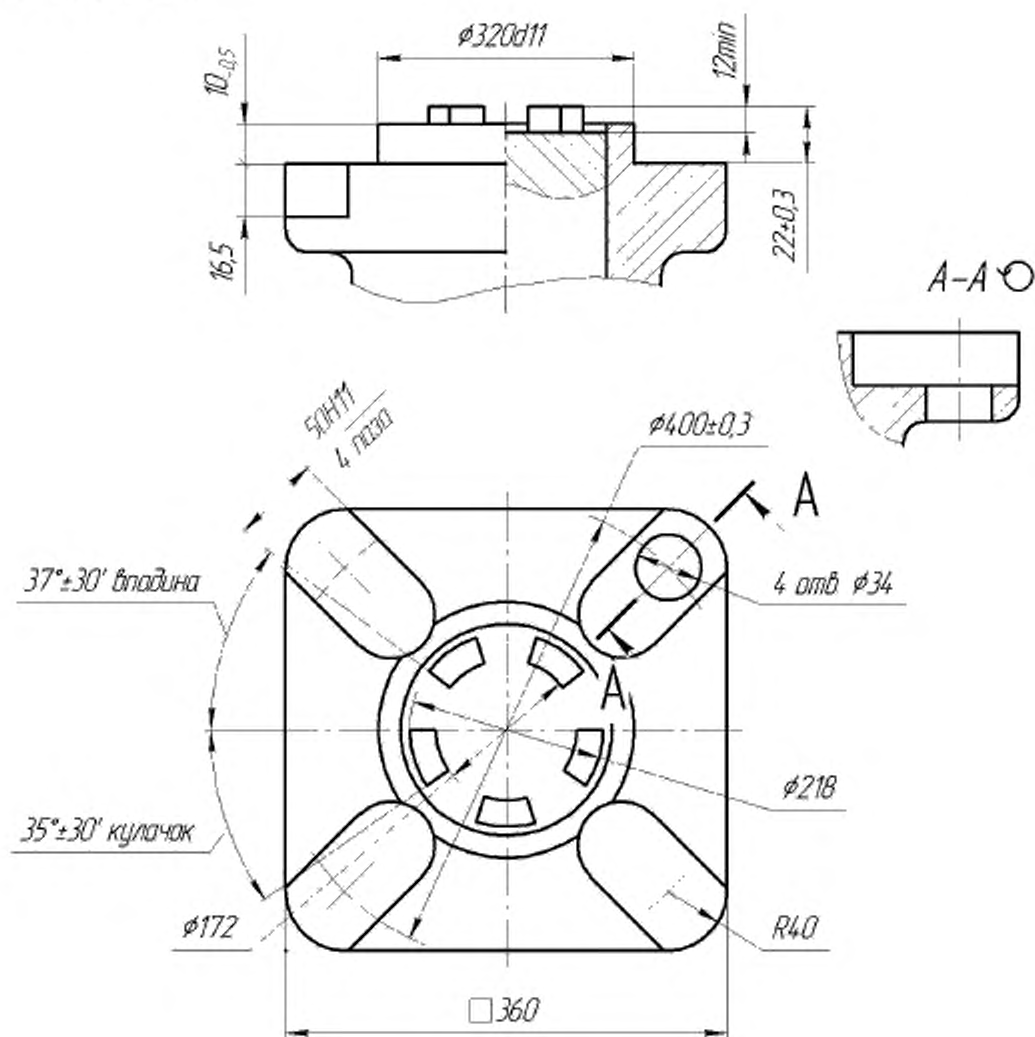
Ответное присоединение трубопроводной арматуры типа Д
